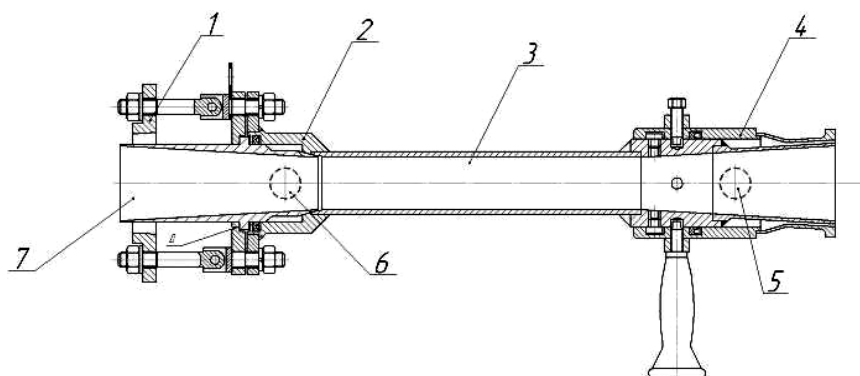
Торкрет-сопло с кольцевым насадком: 1 – обхватный замок подключения бетоновода; 2 – корпус рабочей воздушной камеры; 3 – камера смешения; 4 – корпус кольцевого насадка; 5, 6 – подвод сжатого воздуха; 7 – кольцевой переходник
